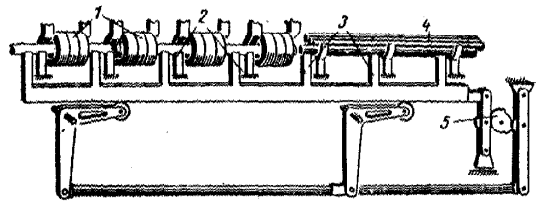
Схема нагревателя с секционированным индуктором и шагающим механизмом для транспортирования заготовок:
